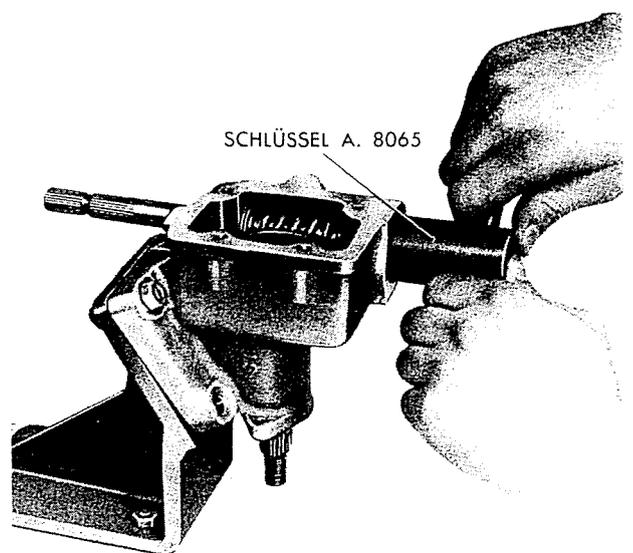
Gewinding zur Befestigung des Rollenlagers und zur Einstellung der Schnecke mit Schlüssel A. 8065 herausnehmen.
